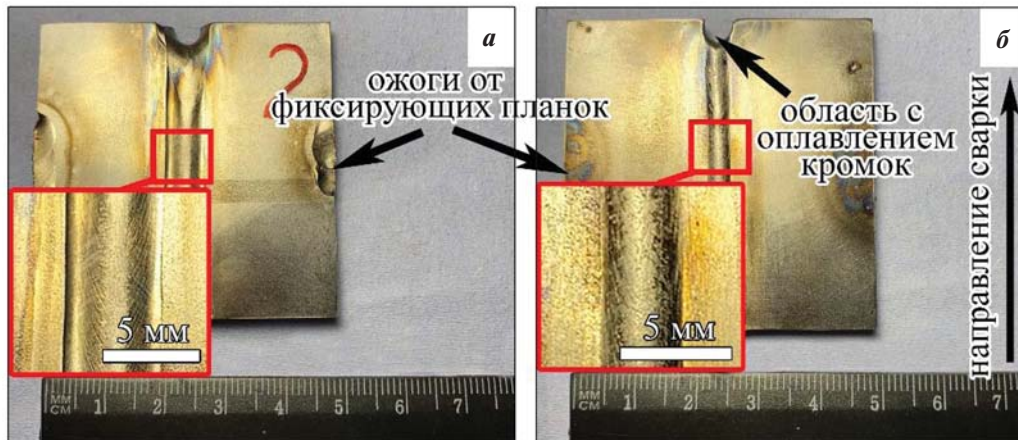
Внешний вид сварного соединения из сплава ВТИ-4, полученного плазменной сваркой проникающей дугой по режиму 4
